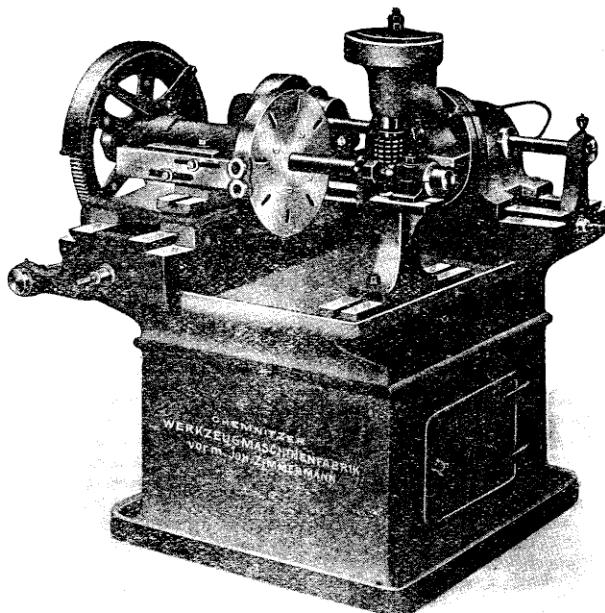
Machine automatique pour la taille continue des engrenages droits.
